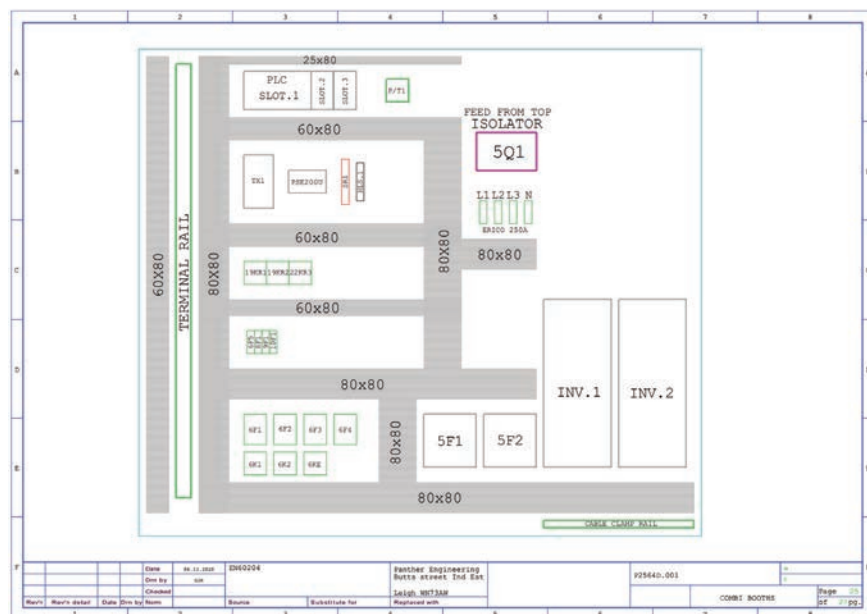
| Cabinet-Layouts lassen sich mit WSCAD einfach erstellen und Schaltpläne aus anderen elektrischen CAD-Systemen können importiert werden.
